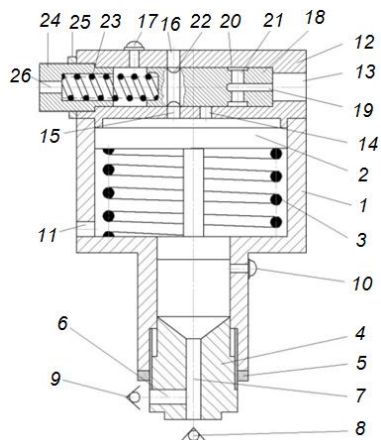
Устройство для автоматического ввода депрессорной присадки:
